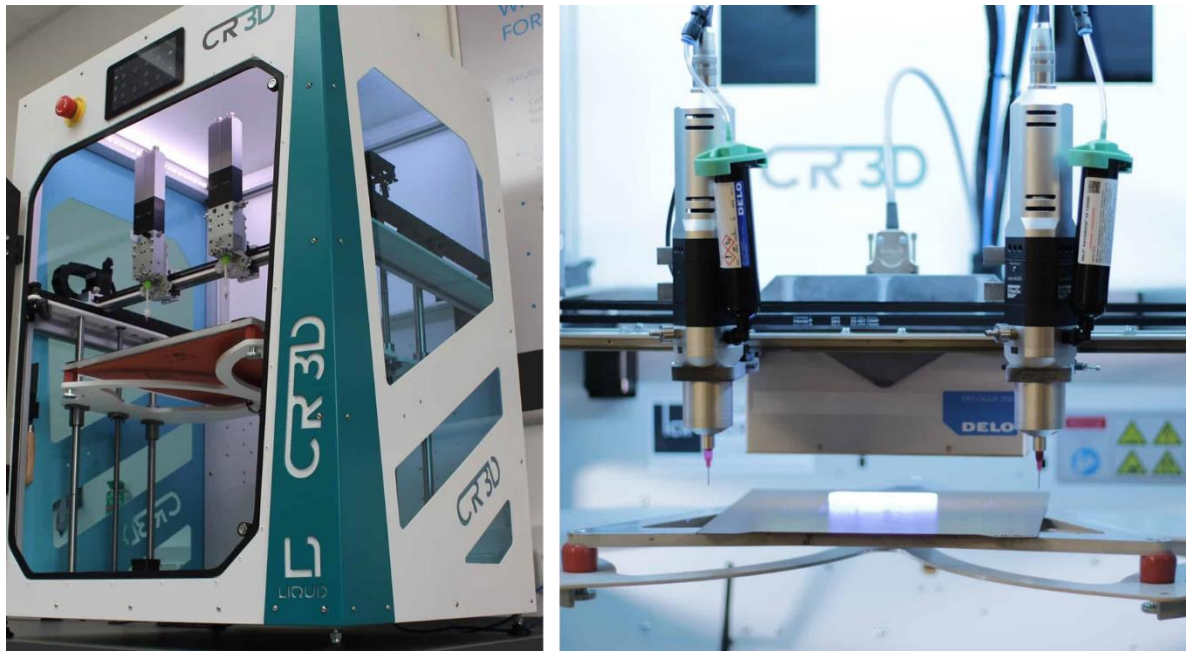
3D-Drucker L1 des Herstellers CR-3D; links: Gesamtansicht; rechts: Detailansicht von zwei montierten Extrusionsmodulen für hochviskose Medien [ING 22]; [ING 21]
